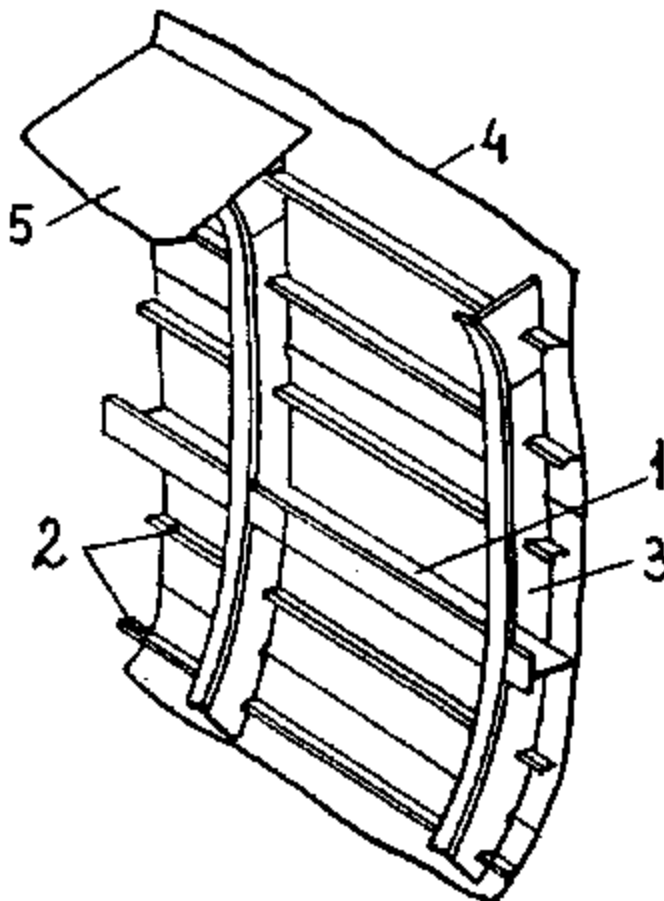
Конструкция бортового перекрытия при продольной системе набора:
